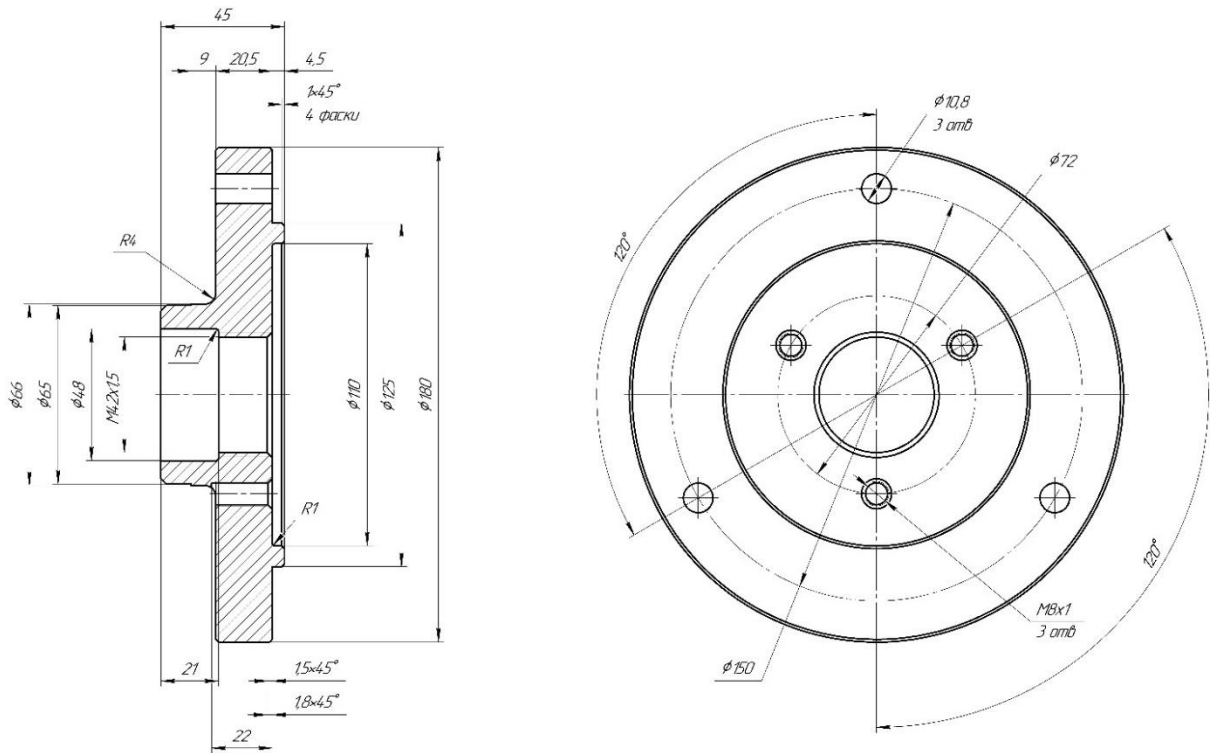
Креслення фланця шпинделя верстата 1П365
